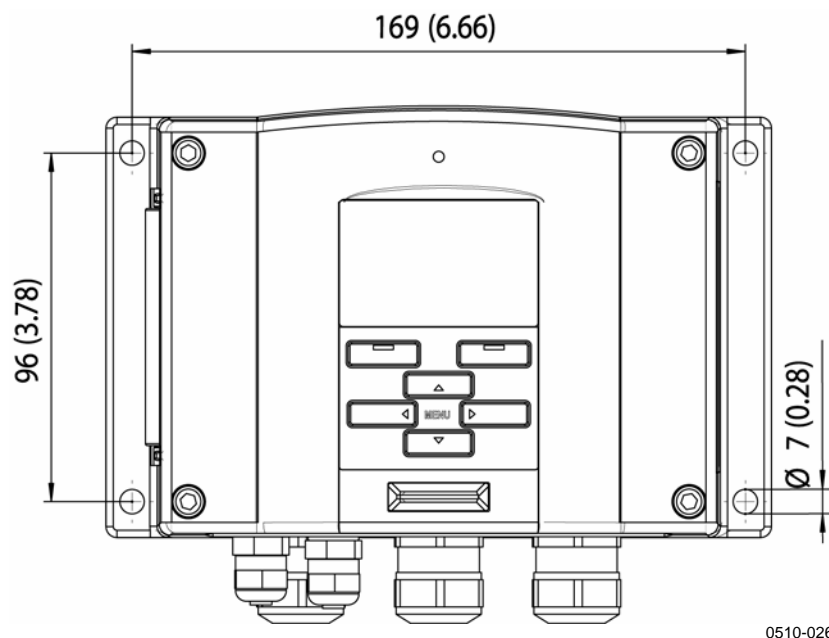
Standard-Montageabmessungen (in mm/Zoll)
